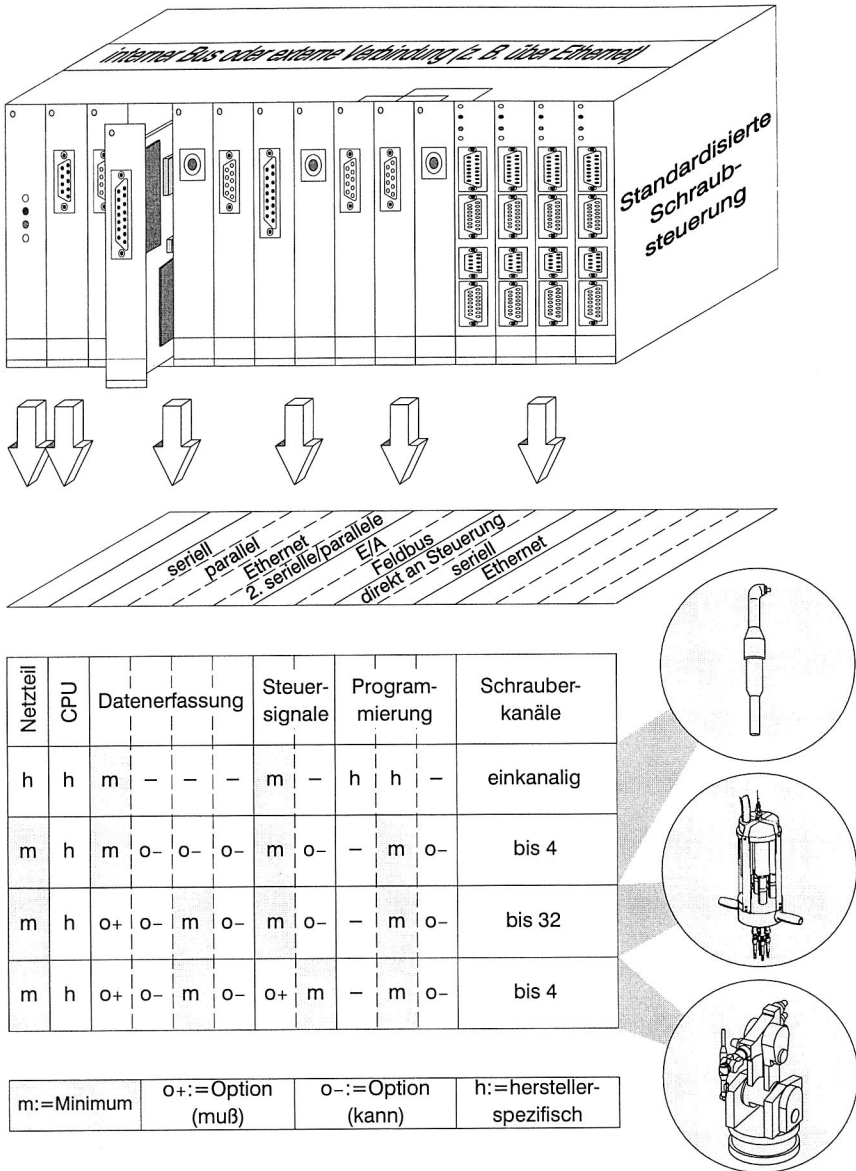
Modular aufgebautes Schraubsteuerungssystem mit standardisierten Schnittstellen
